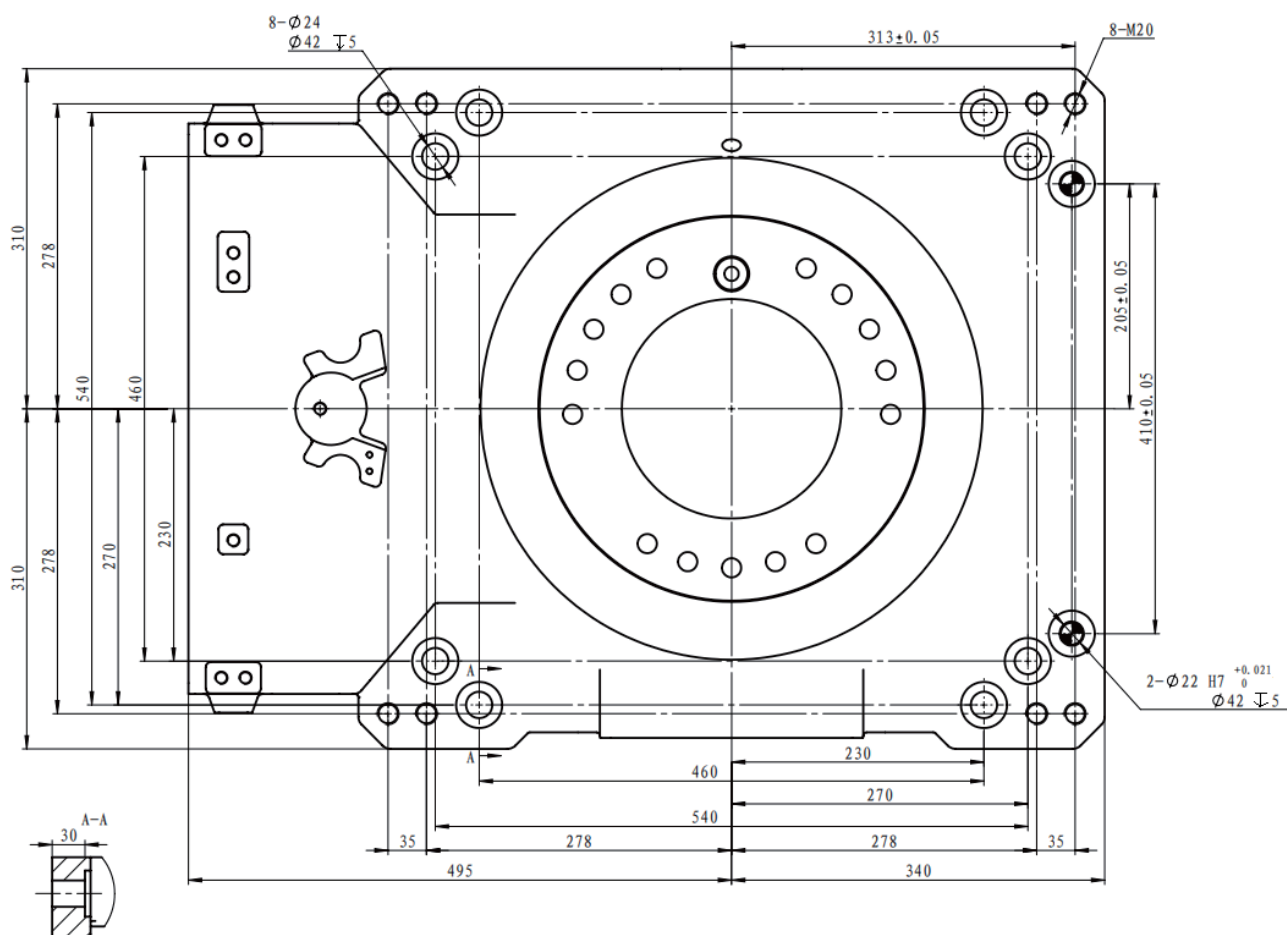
Габаритные чертежи робота-манипулятора SR280-2850.
